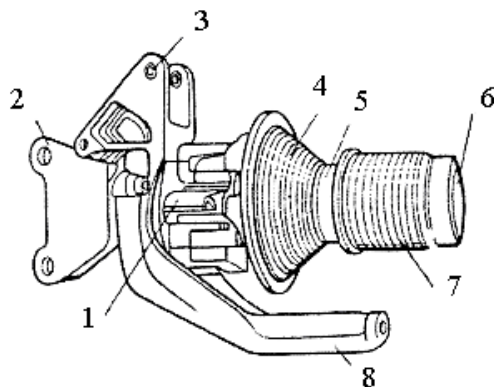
Рукав втулки вертолёта с эластомерными подшипниками.
